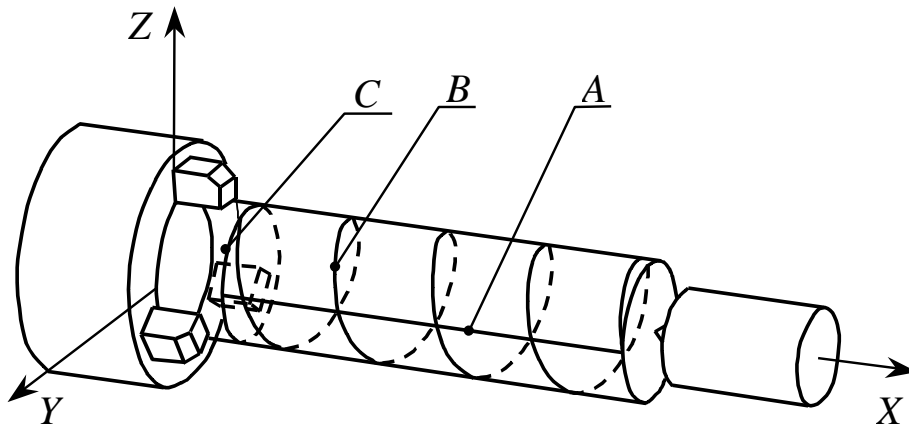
Можливі траєкторії руху вимірювального інструмента навколо деталі циліндричної форми
